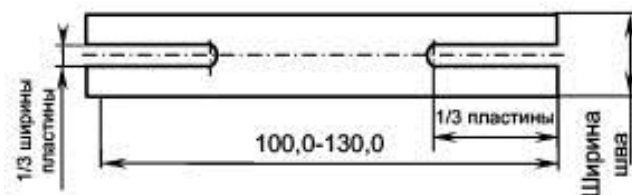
Конструктивные размеры ПП для приварки выводов ЭХЗ к кольцевому стыковому сварному шву МГ
